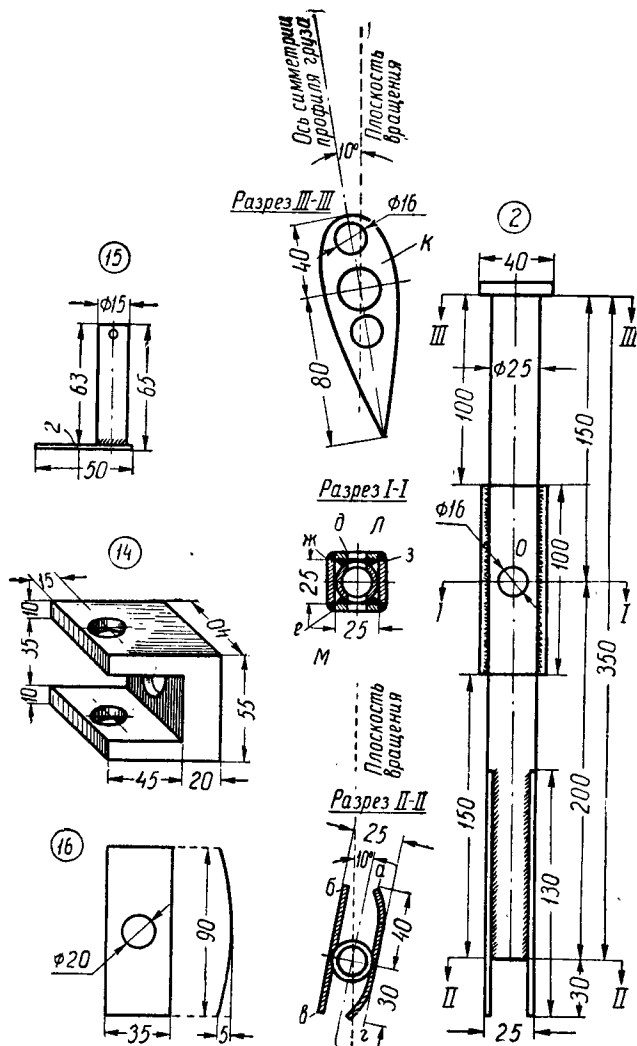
Детали ступицы ветроколеса: 2 — металлическая труба; 14 — скоба; 15 — ось шарнира; 16 — пружина
